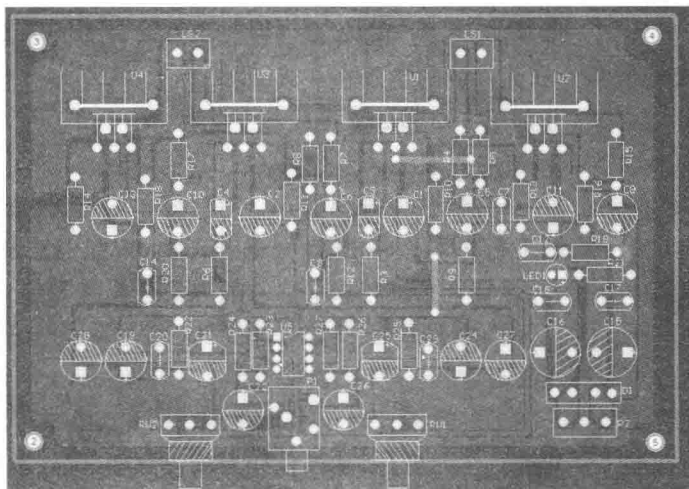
双声道 BTL 功放电路 PCB 布线图
